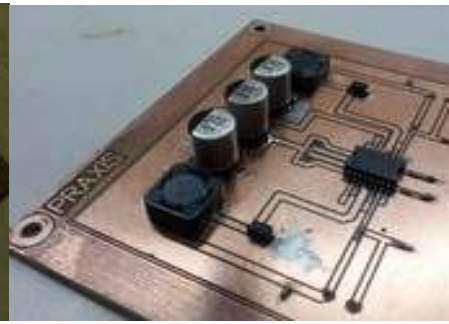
PCB del módulo de alimentación con los componentes soldados
